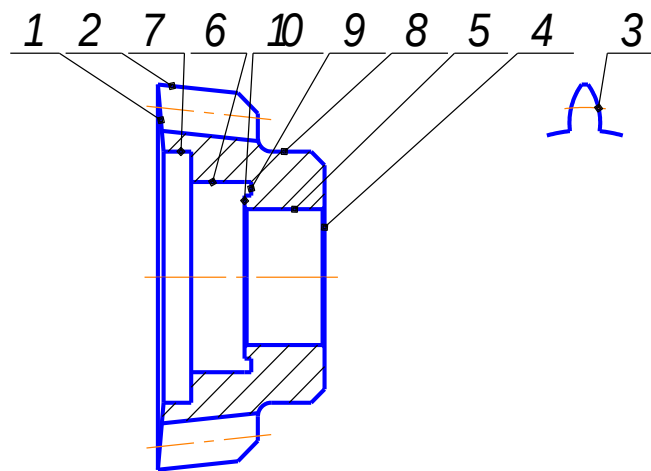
Довбач чашковий: 1 – передня поверхня, 2 – задня поверхня, 3 – бокова поверхня зуба, 4 – торець, 5 – отвір, 6 – виточка, 7 – канавка виточки, 8 – ступиця, 9 – канавка торця виточки, 10 – торець виточки
